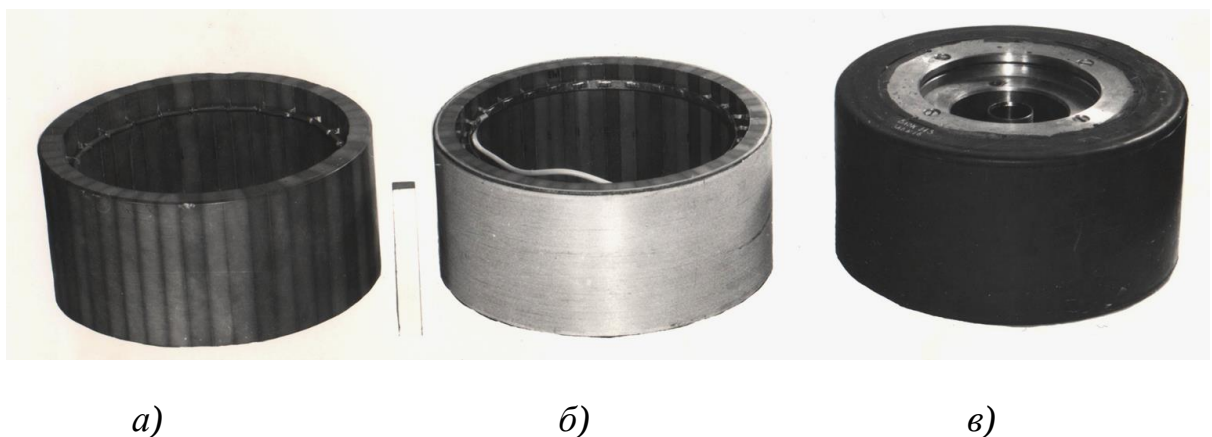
Варіанти конструкцій циліндричного перетворювача [1]
